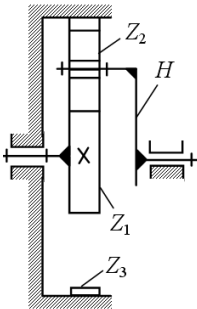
Планетарный механизм с одинарным сателлитом
